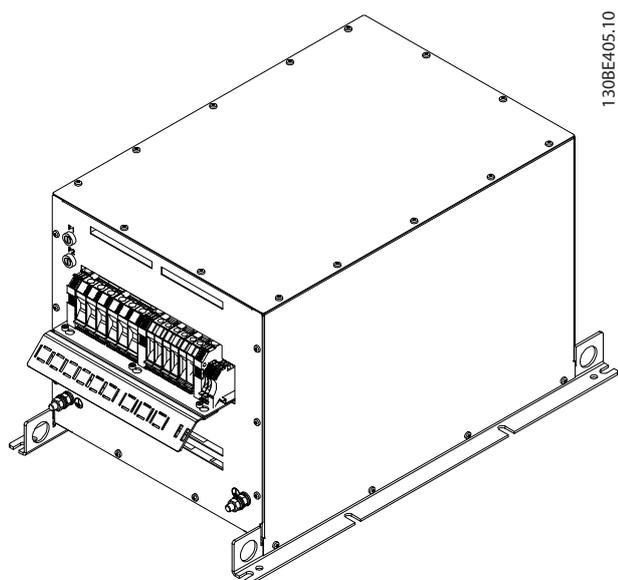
IP20 X4, внешний вентилятор 1, 3D-вид
